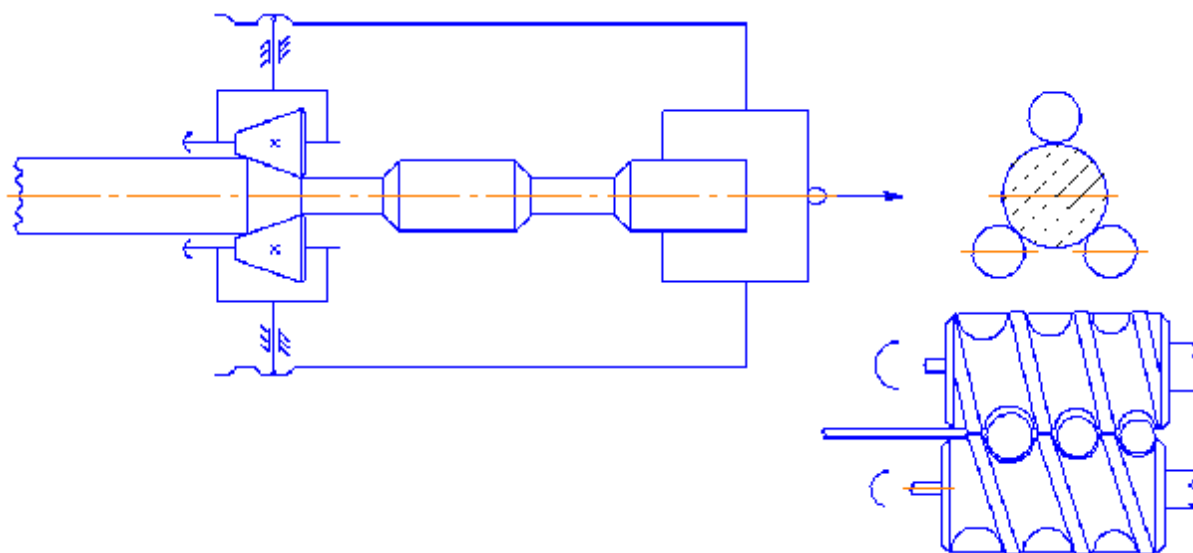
Схема поперечно – винтовой прокатки шаров
